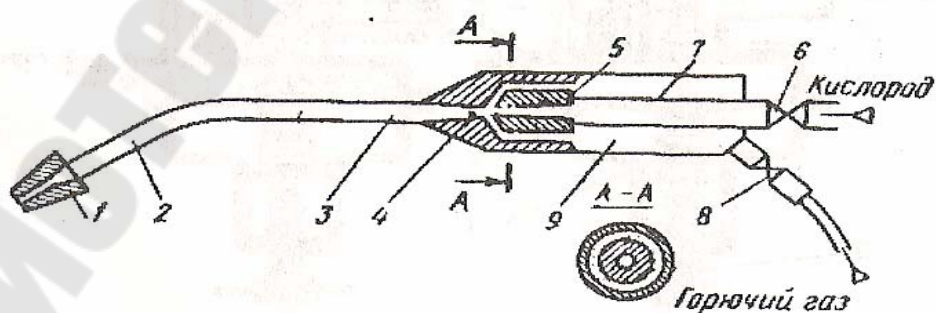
Схема газовой горелки: 1 – мундштук; 2 – наконечник; 3 – смесительная камера; 4 – инжекторная камера; 5 – канал подачи горячего газа; 6 – кислородный вентиль; 7 – канал подачи кислорода; 8 – газовый вентиль; 9 – корпус горелки
